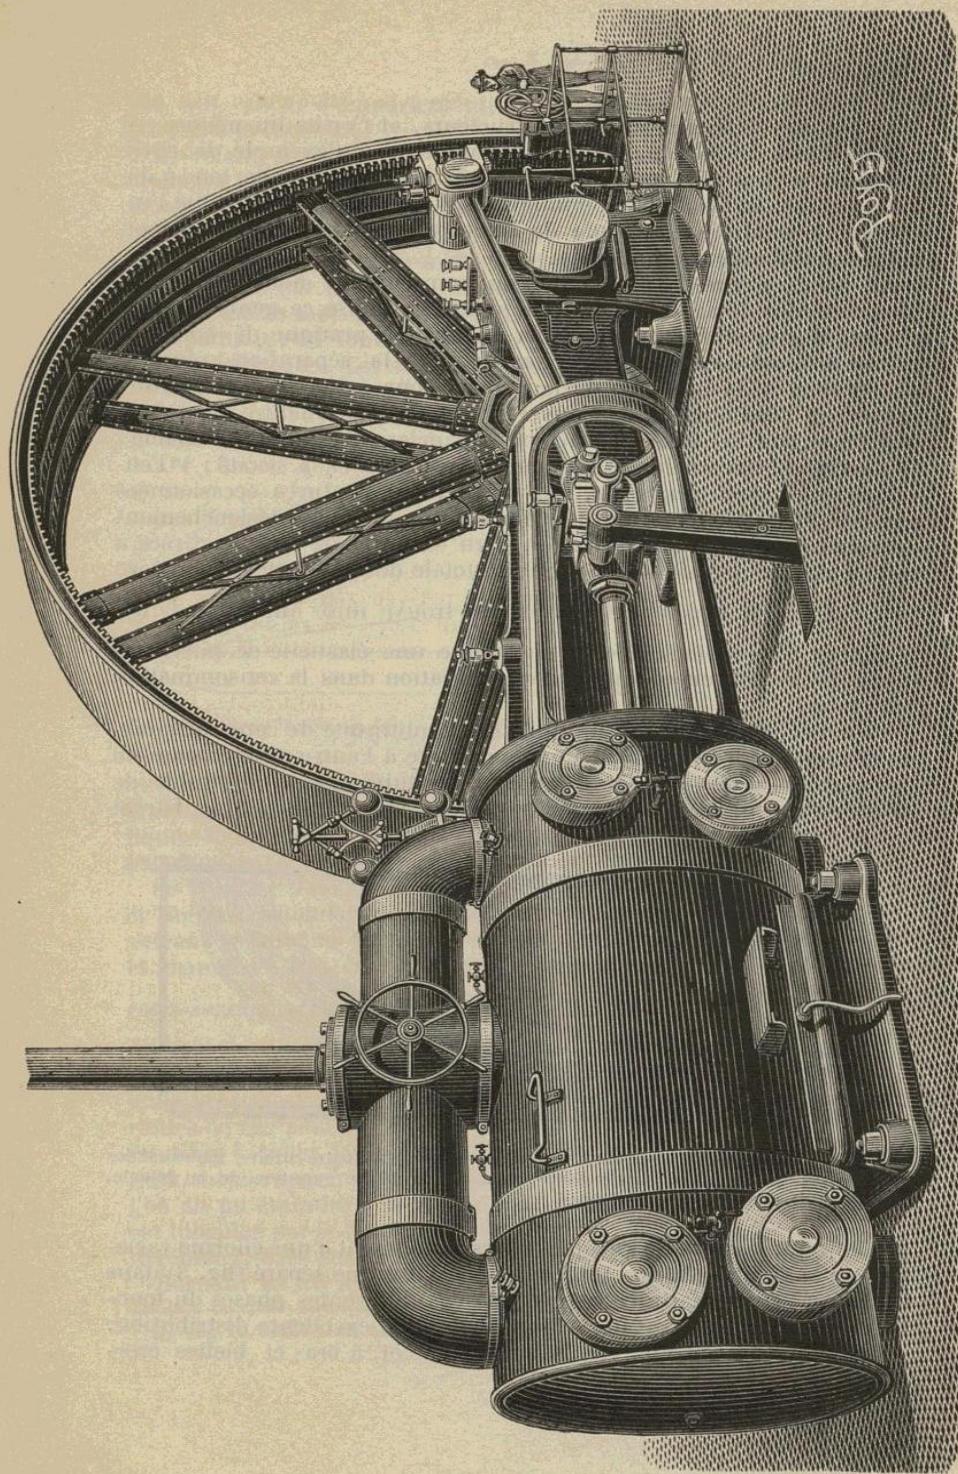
La machine à vapeur de 4 000 chevaux du Palais des Machines à l'Exposition de 1889.
